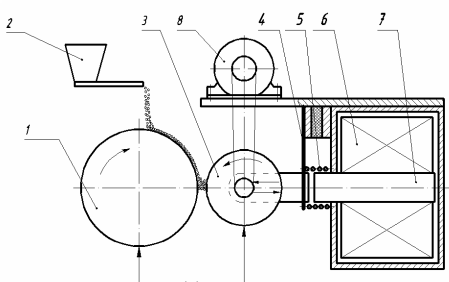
Устройство с принудительно вращающимся осциллирующим наконечником: 1 – обрабатываемая деталь; 2 – дозирующее устройство; 3 – самовращающийся наконечник; 4 – гибкая металлическая пластина; 5 – пружина; 6 – электромагнитная катушка; 7 – сердечник; 8 – электродвигатель
